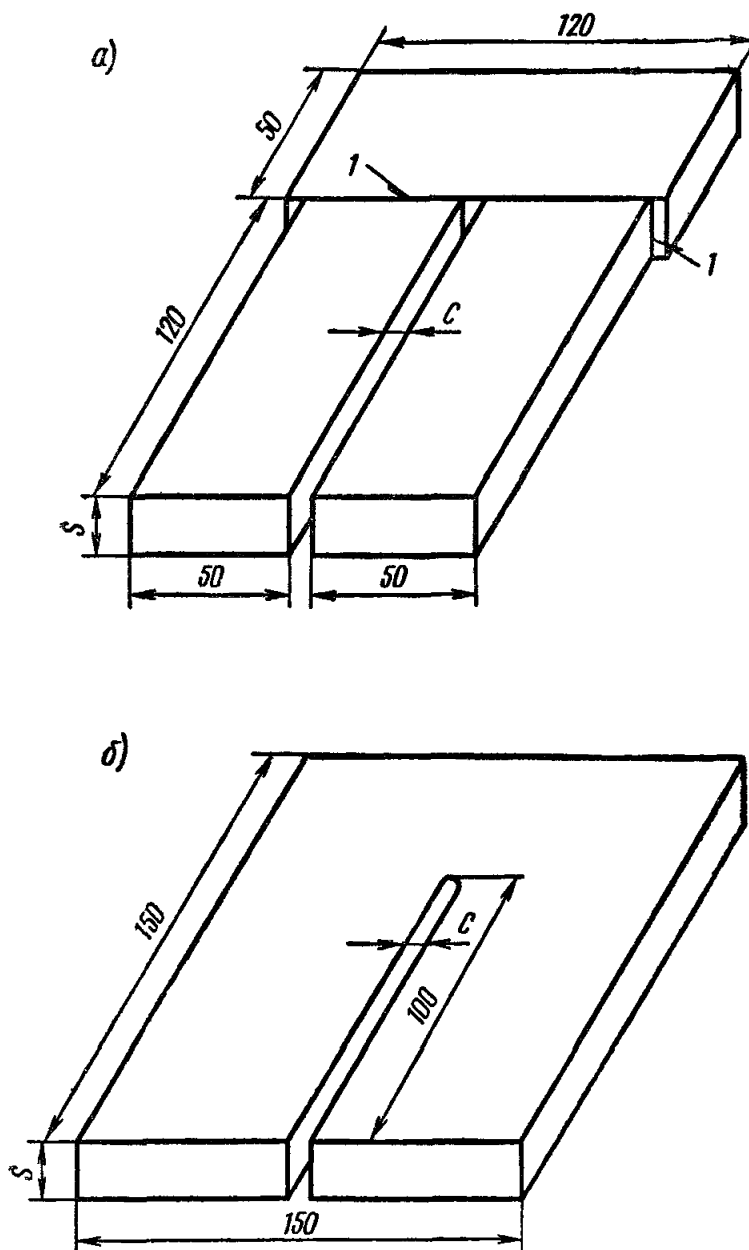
Схема выводных планок для сварки с металлохимической присадкой:
